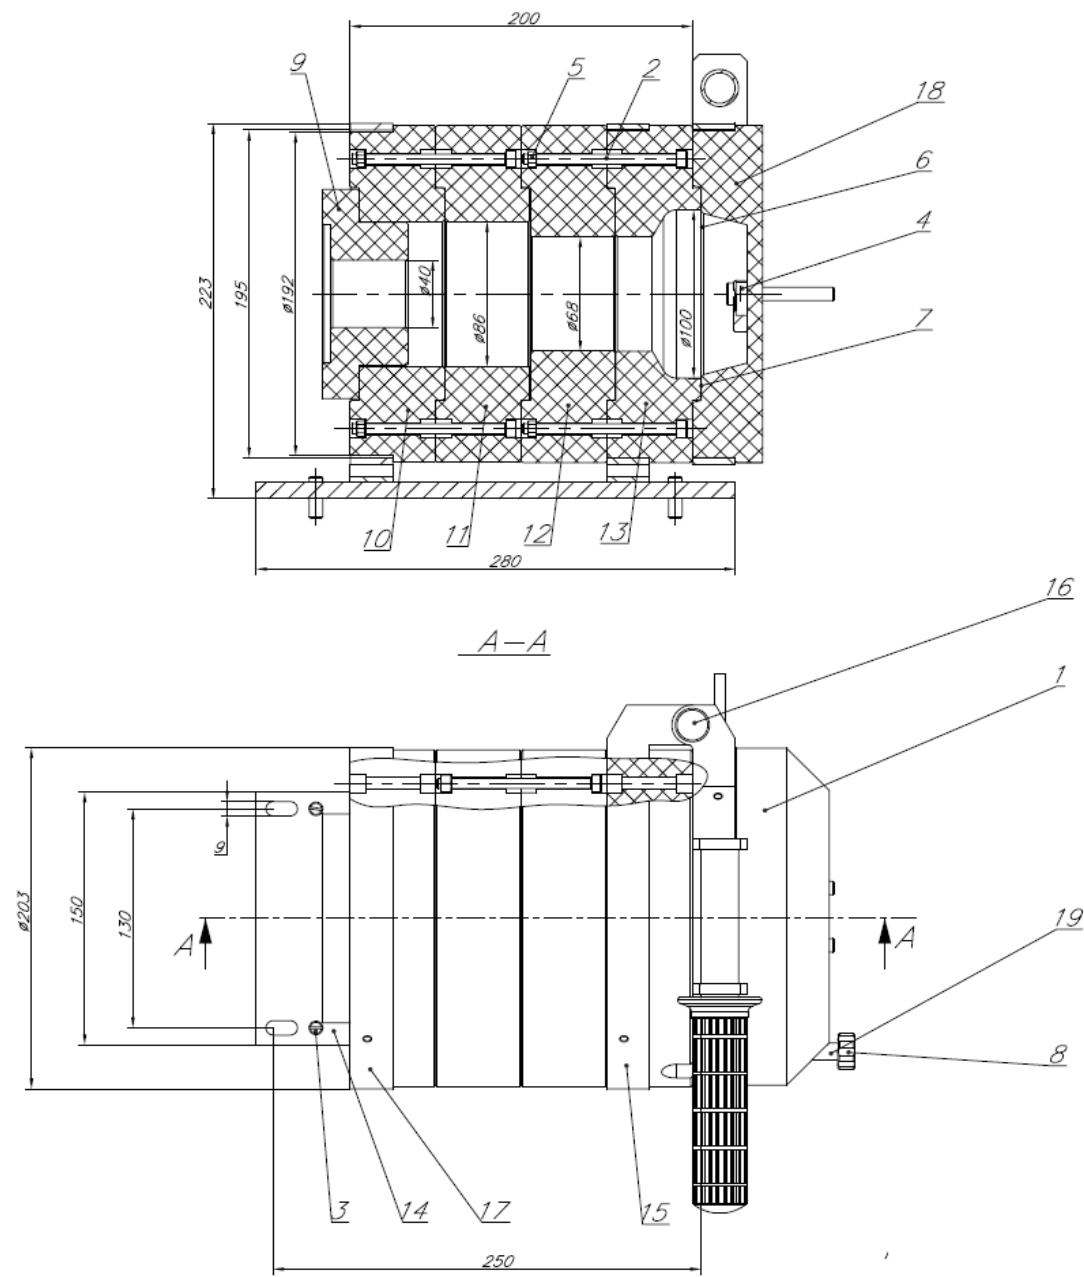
Сборочный чертеж КИ-1001.
